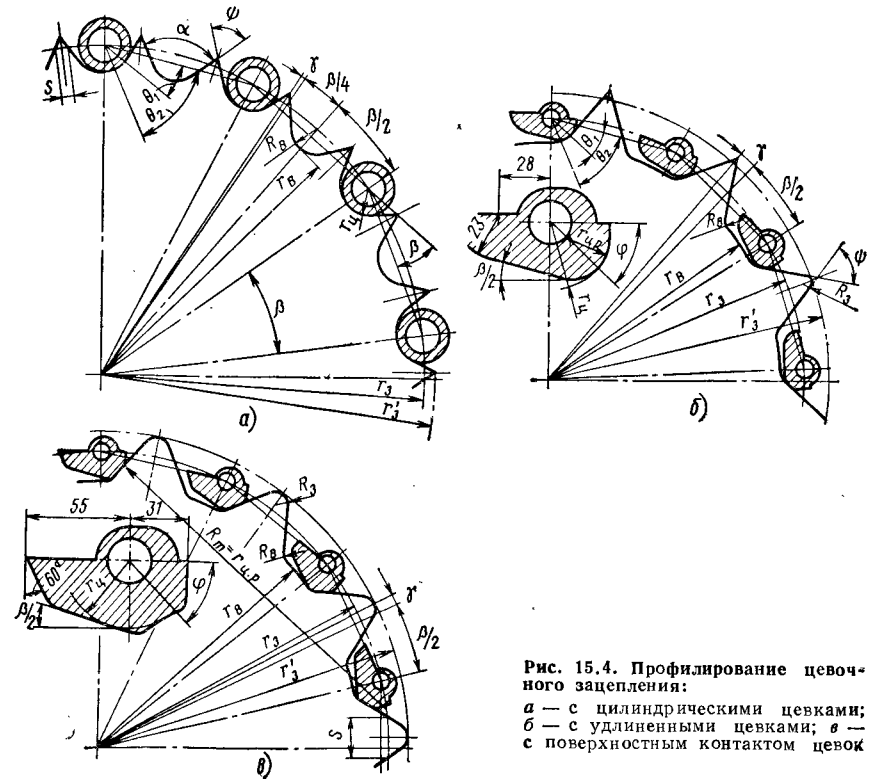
Профилирование цевочного зацепления: а — с цилиндрическими цевками; б — с удлиненными цевками; в — с поверхностным контактом цевок
